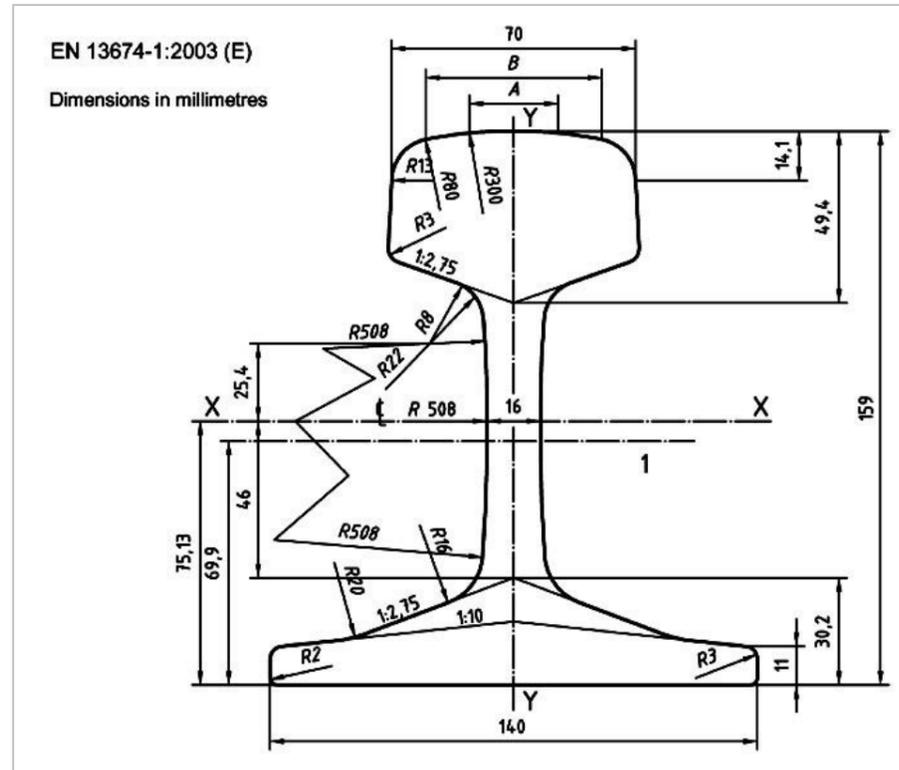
Sección transversal carril 54-E1. Fuente: railwayrail.com
